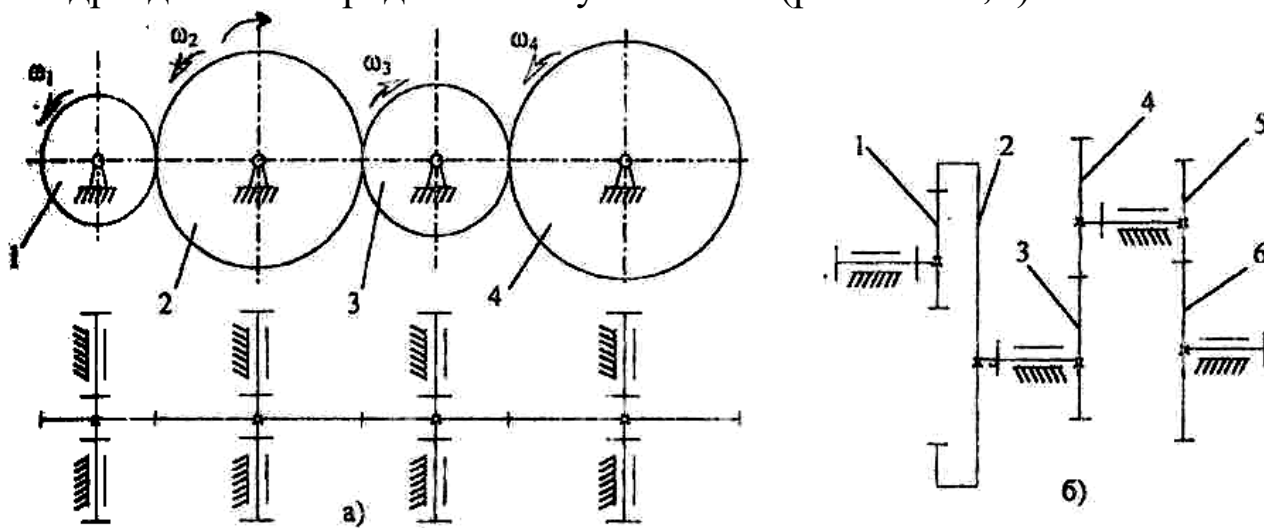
Схемы многозвенных зубчатых механизмов: а – рядовая (с паразитными колесами), б - ступенчатая
